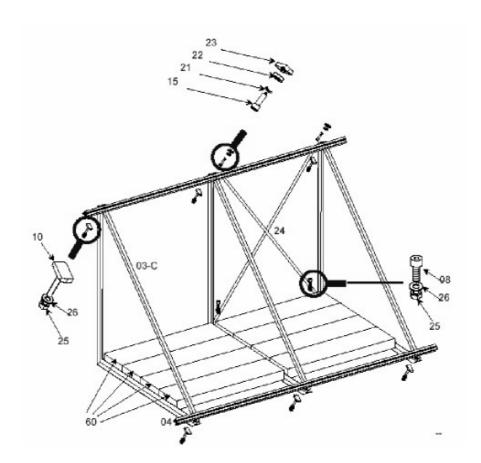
Exemple de support pour montage sur toiture terrasse ou au sol avec lest en dalles de béton
